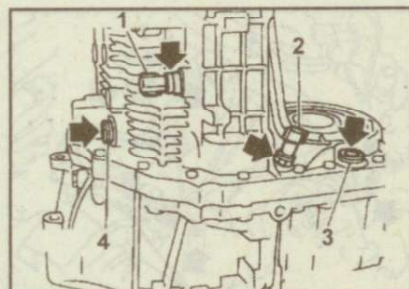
Расположение выключателя лампы света заднего хода (1), выключателя PNP (2), пробки слива (3) и заливки (4) трансмиссионного масла
